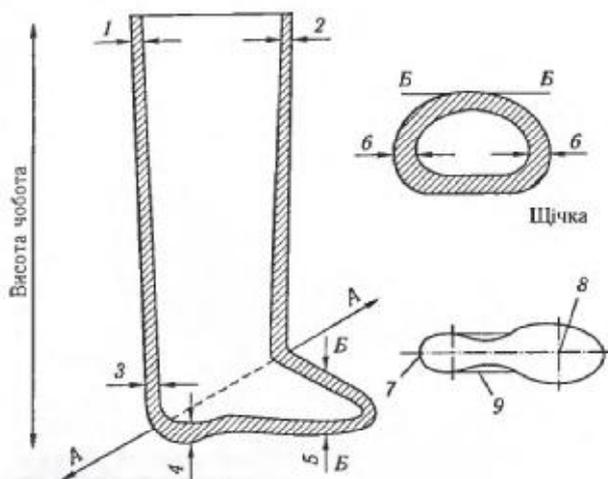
Точки вимірювання валяних чобіт: 7 — п'яткова; 8 — підметкова; 9 — суліяторна
